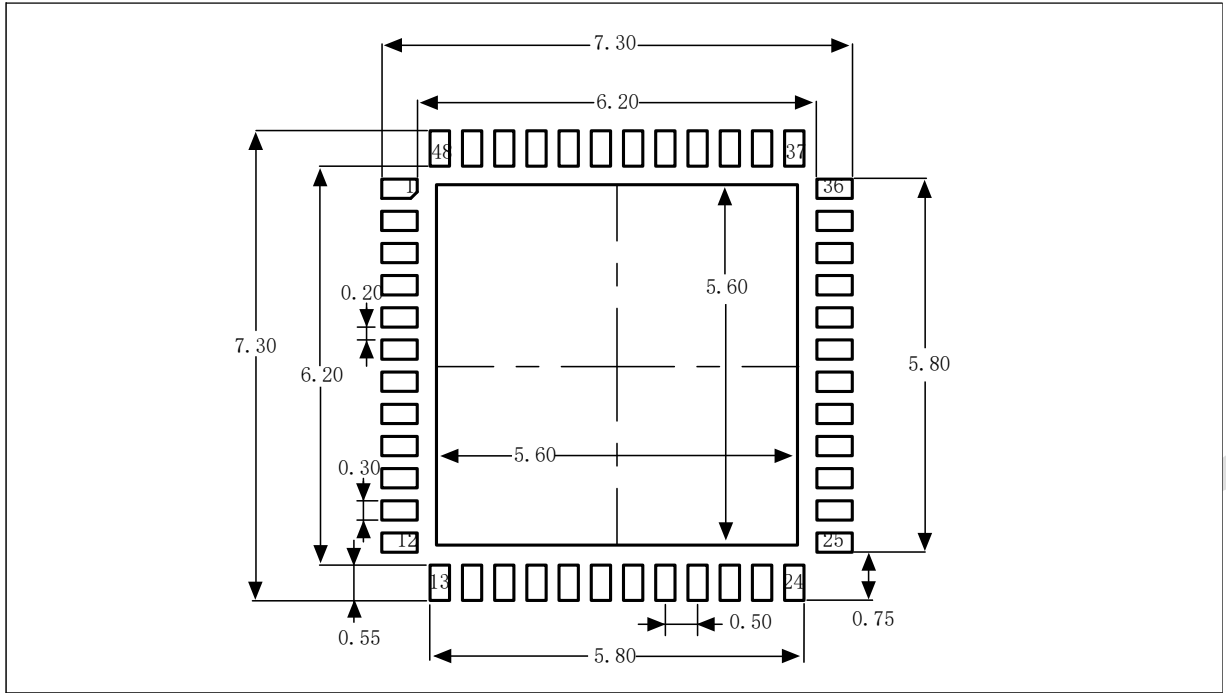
QFN48 芯片的 PCB 安装尺寸图
